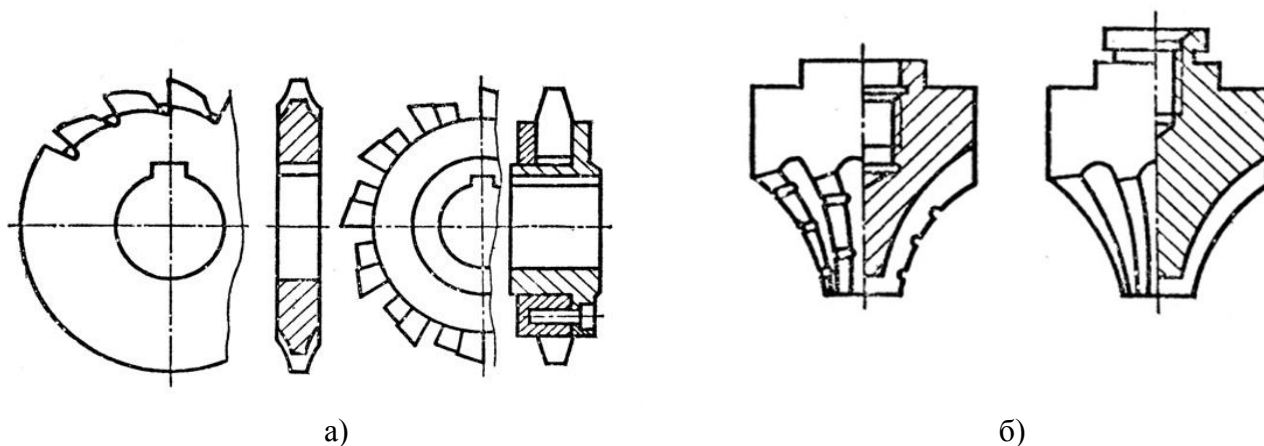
Модульные фрезы для нарезания зубчатых колес методом копирования:
